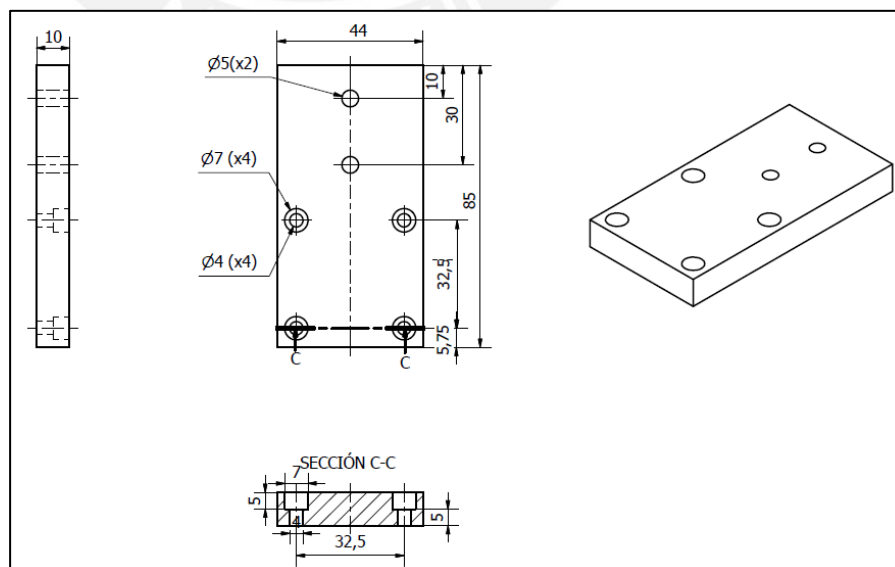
Unión entre Actuador DPZ y DGEA
